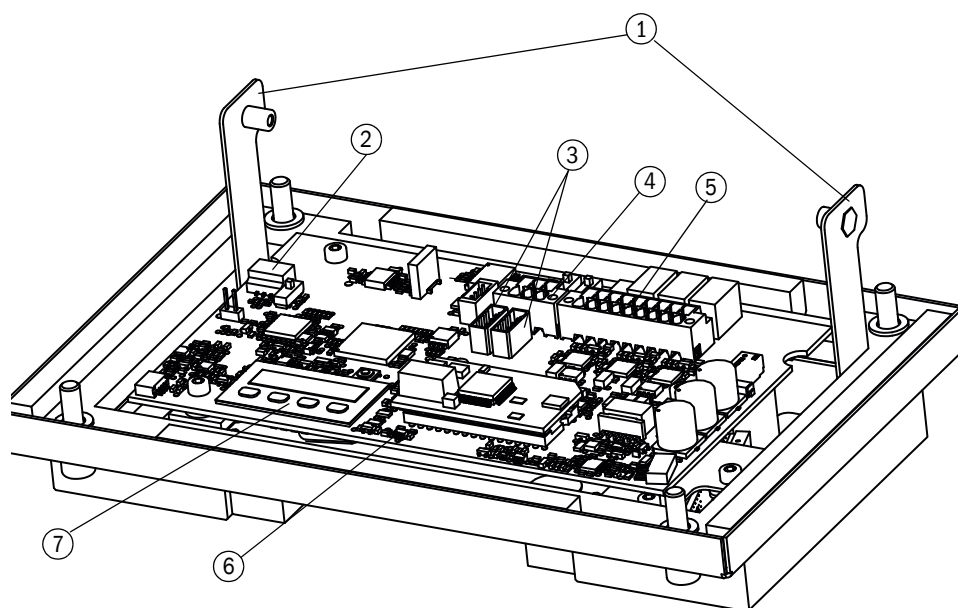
Вид внутри - крышка корпуса без нагревателя
